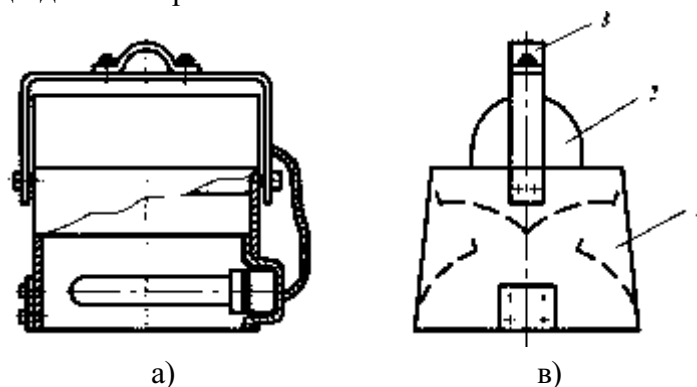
Елементи конструкції опромінювача ЖСП18-400-001-ХЛ4: 1 – корпус з дзеркальним відбивачем; 2 – блок ПРА; 3 – вузол підвісу
